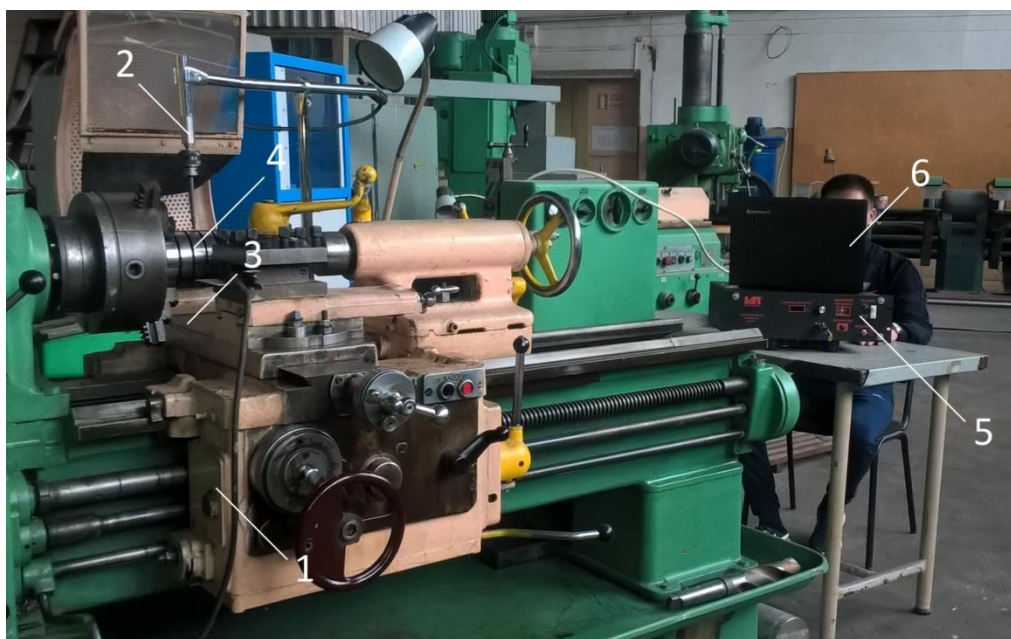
Процесс получения значений шероховатости профилметром стали 30ХГСА
